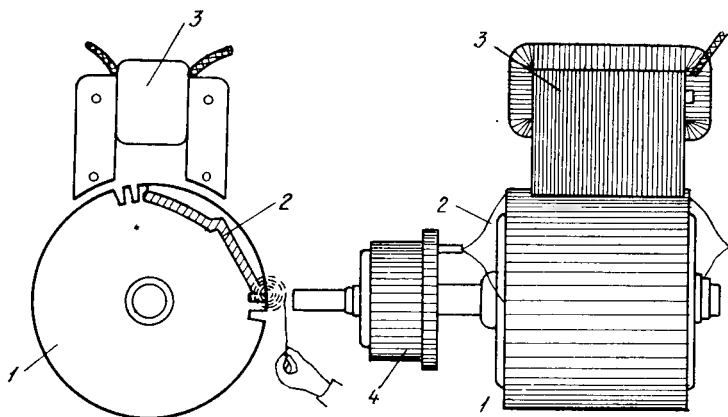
Электромагнит для проверки якорей на витковое замыкание:
